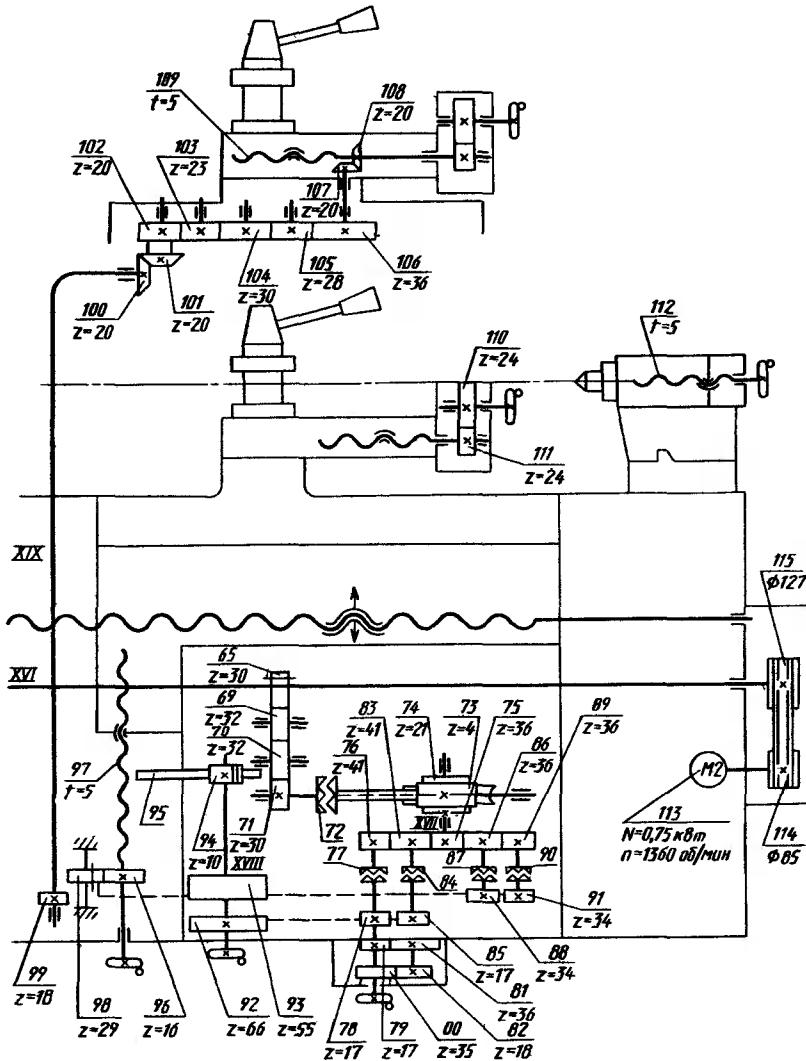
Кинематическая схема современного токарно-винторезного станка модели 16К20
